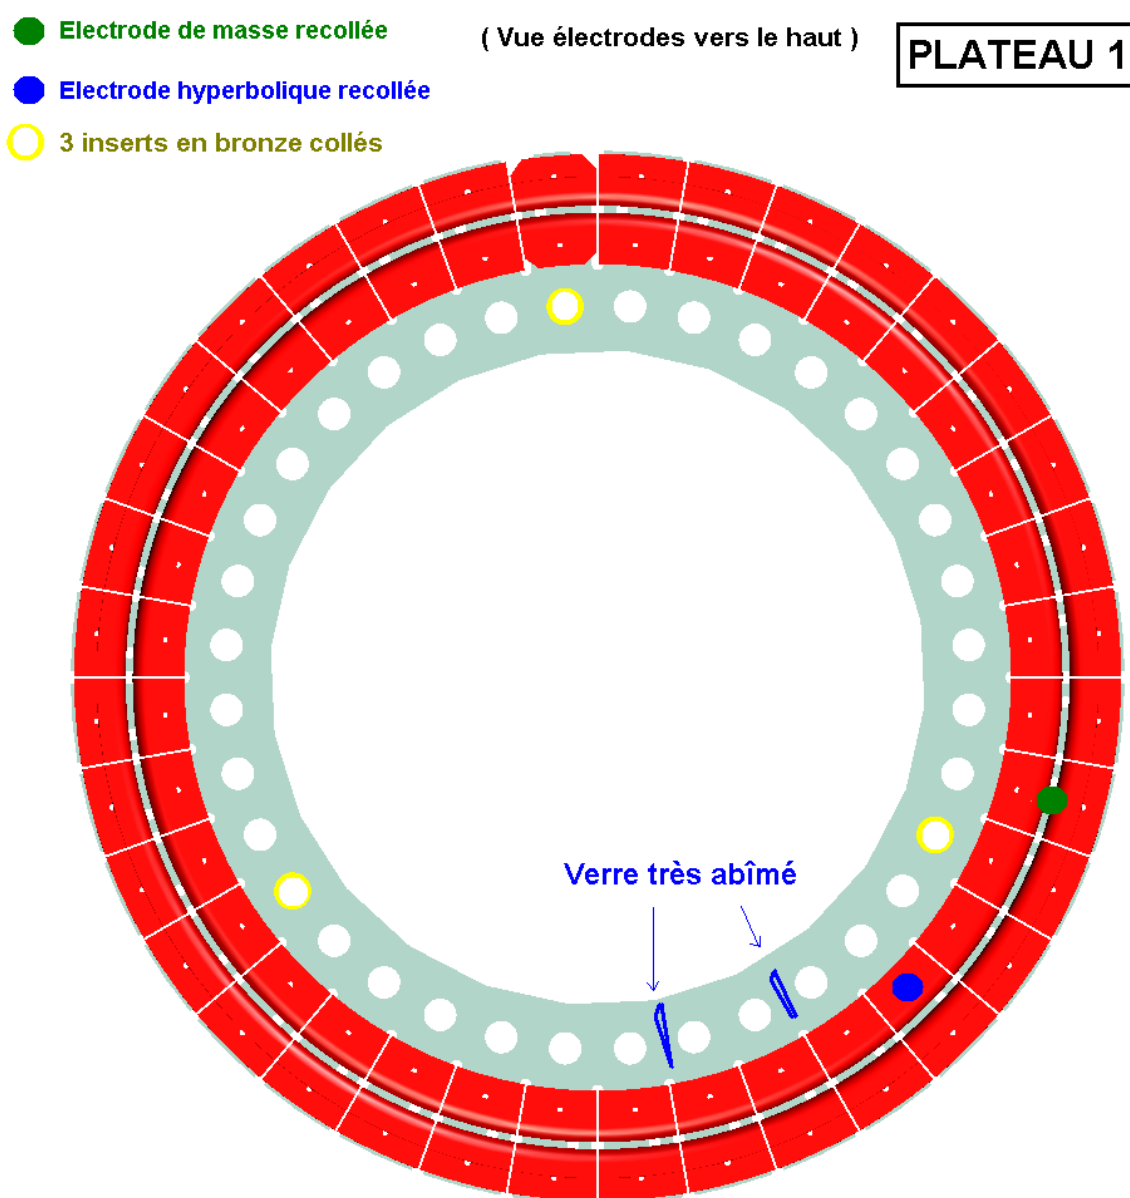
Défauts d'assemblage des électrodes du haut
